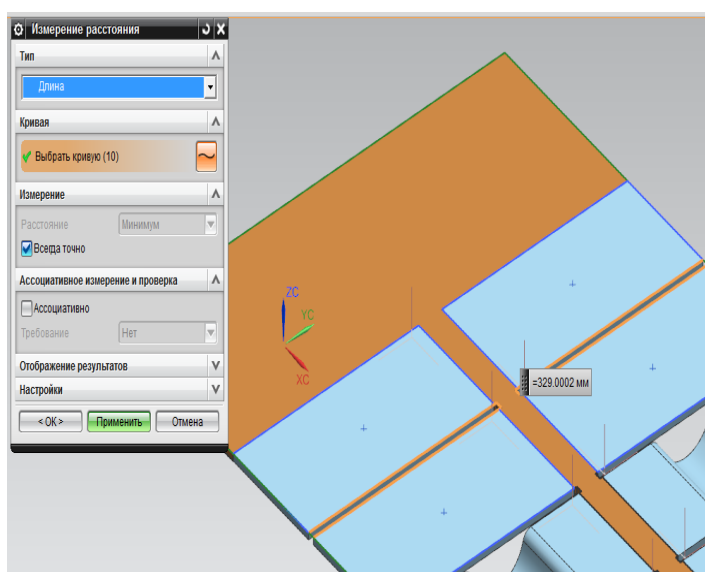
Длина линии реза предлагаемой заготовки
